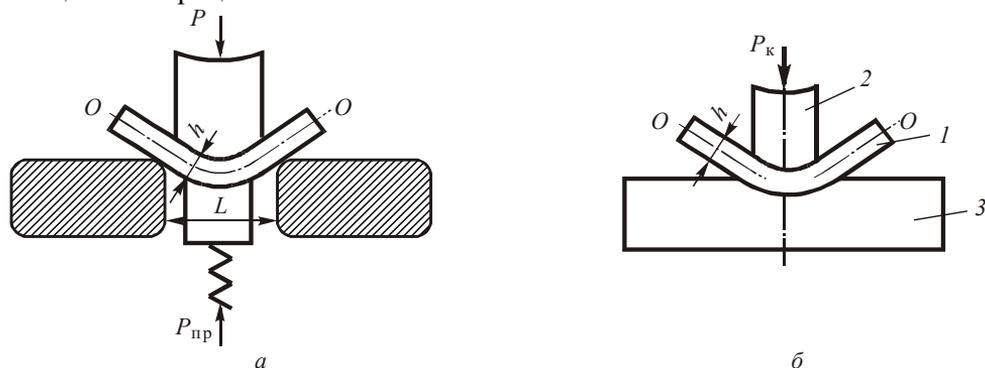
Схемы гибки с прижимом (а) и с калибровкой (б)
